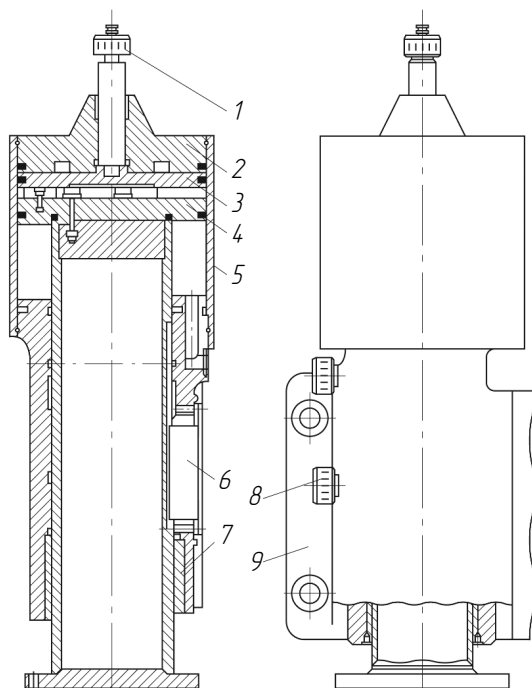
Пневматичний привід стискання електродів машин точкового зварювання
